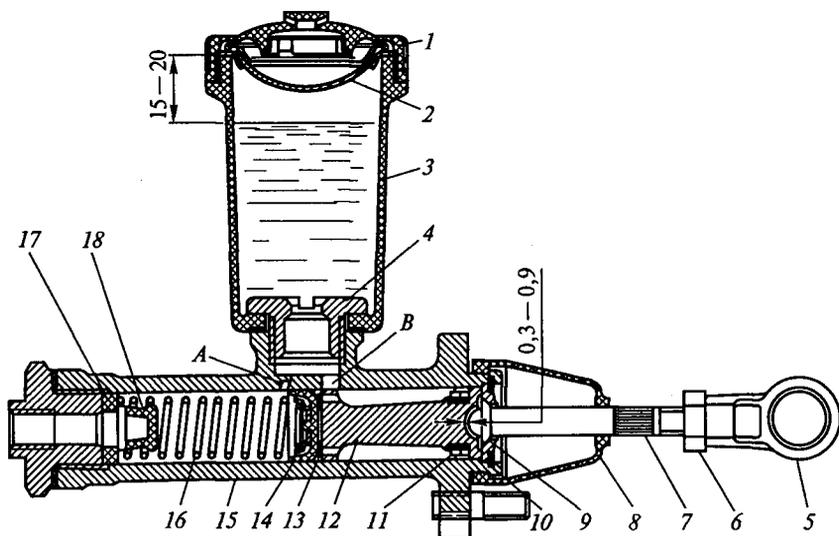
Главный цилиндр привода выключения сцепления:
